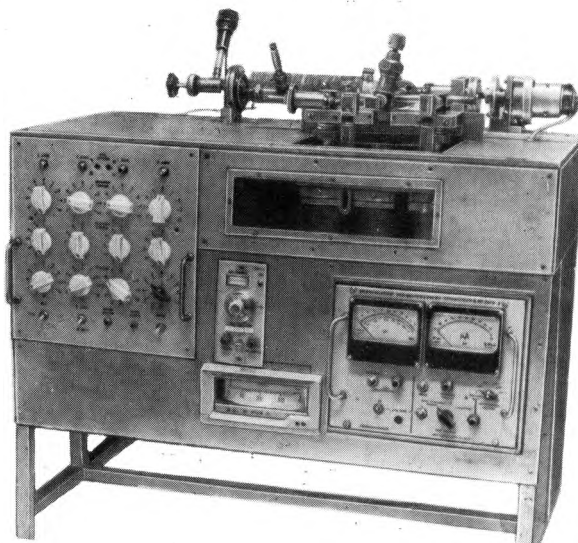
Установка молекулярного наплаивания (УМН-1)
